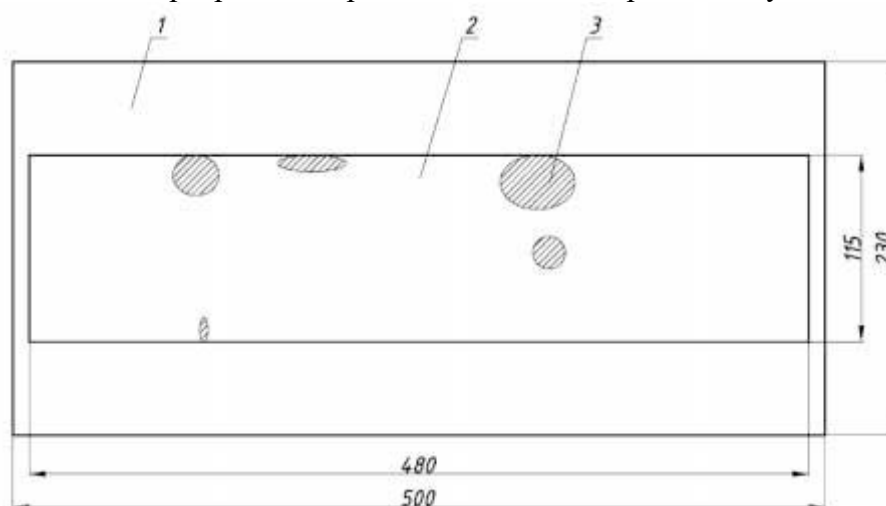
Схема сварного шва зон в биметалле сталь-медь, полученном по режиму 3:
